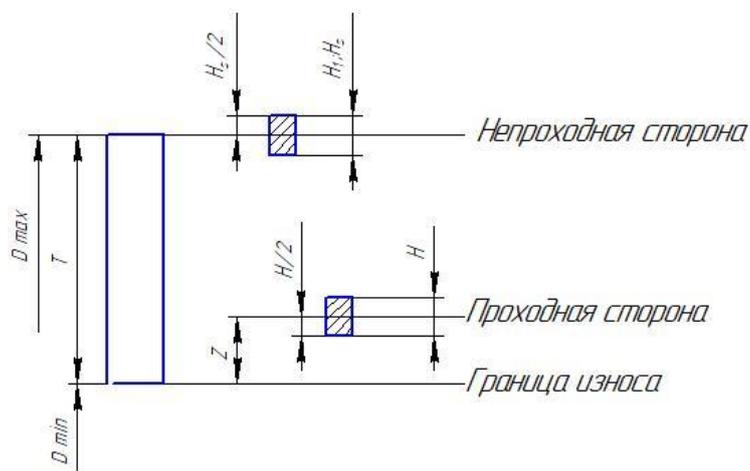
Схема расположения полей допусков калибров для контроля отверстий.
